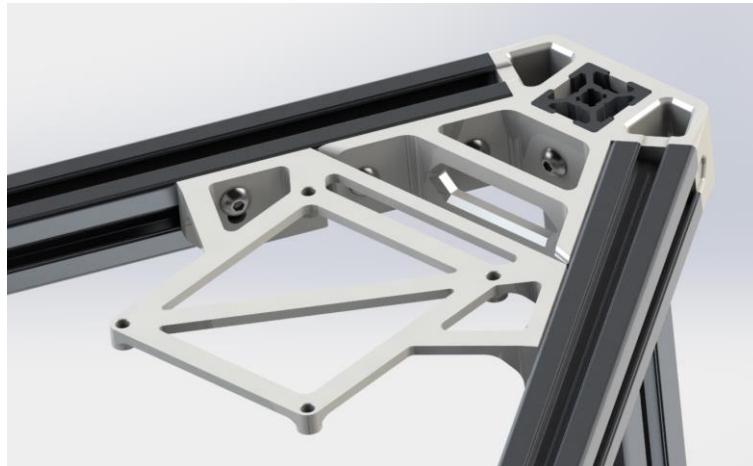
Detalle ensamblaje final de carrera SolidWorks®.
